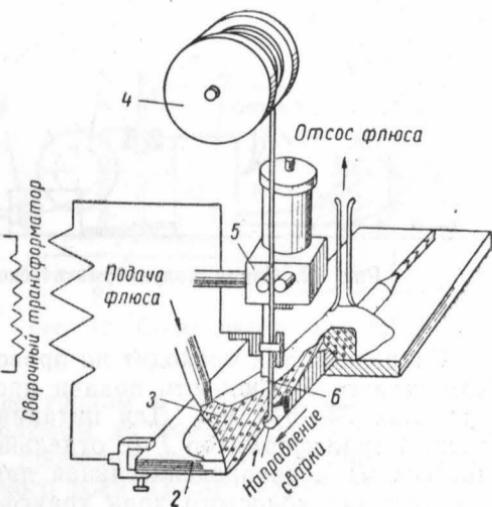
Схема процесса автоматической сварки под флюсом
